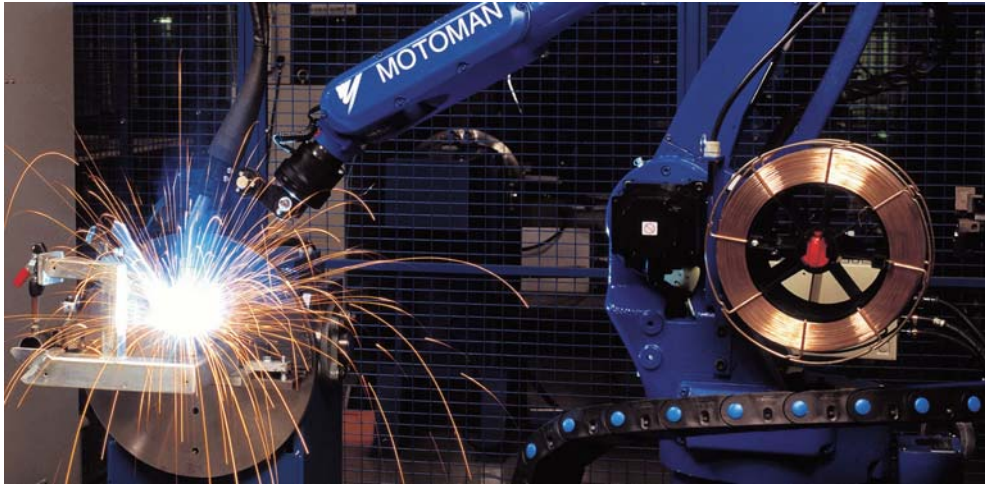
Robot antropomórfico estándar con equipamiento de soldadura al arco.
